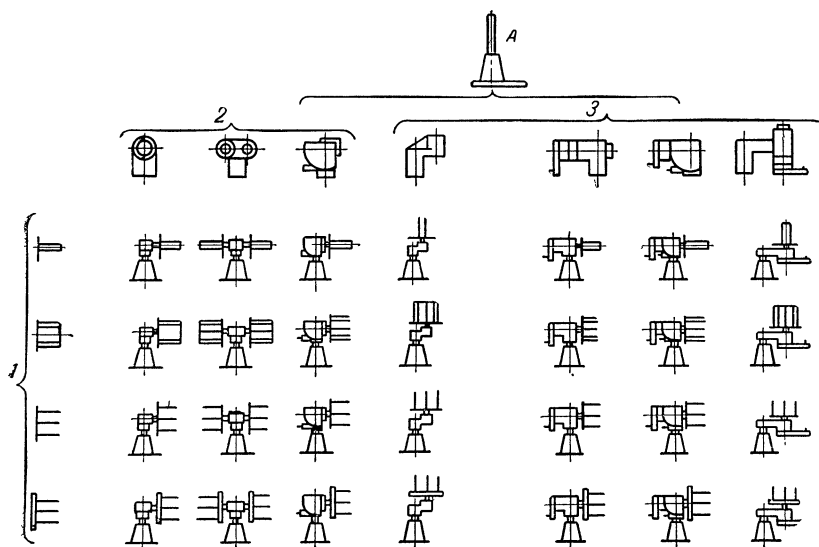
Варианты компоновки агрегатного разматывающего устройства.
